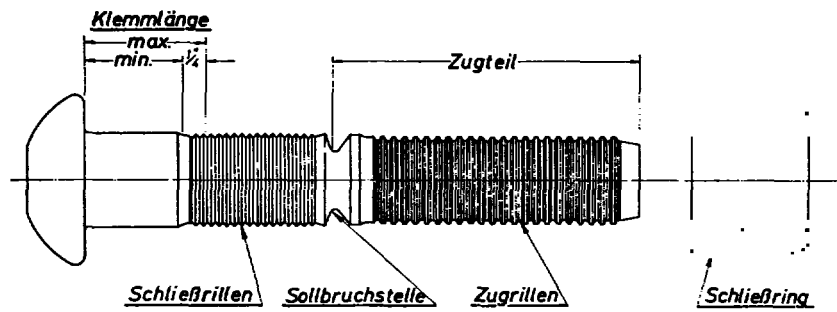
Zu einem gebräuchlichen Schließringbolzen-System gehörender Bolzen mit Schließring
